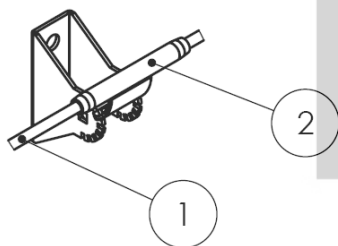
Montaje del cable en un punto de anclaje estructural intermedio sobre pared. Partes: 1- cable, 2- punto de anclaje estructural intermedio.
